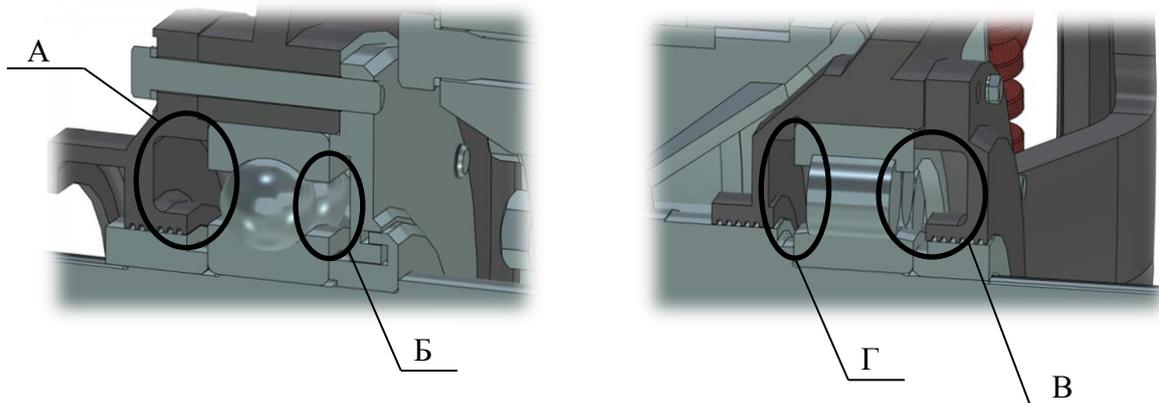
Пополнение смазки в подшипниковых узлах
